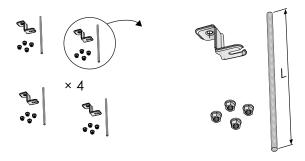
Élément d'assemblage SYST MS M8-1, montage au plafond et sur tige filetée
